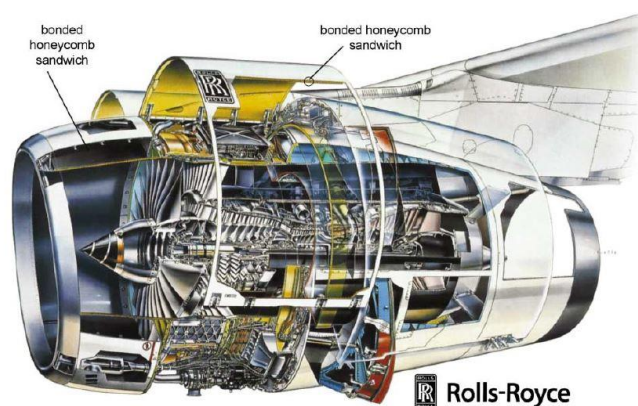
Vista em corte de um motor de avião usando painéis sandwich colados [8].
